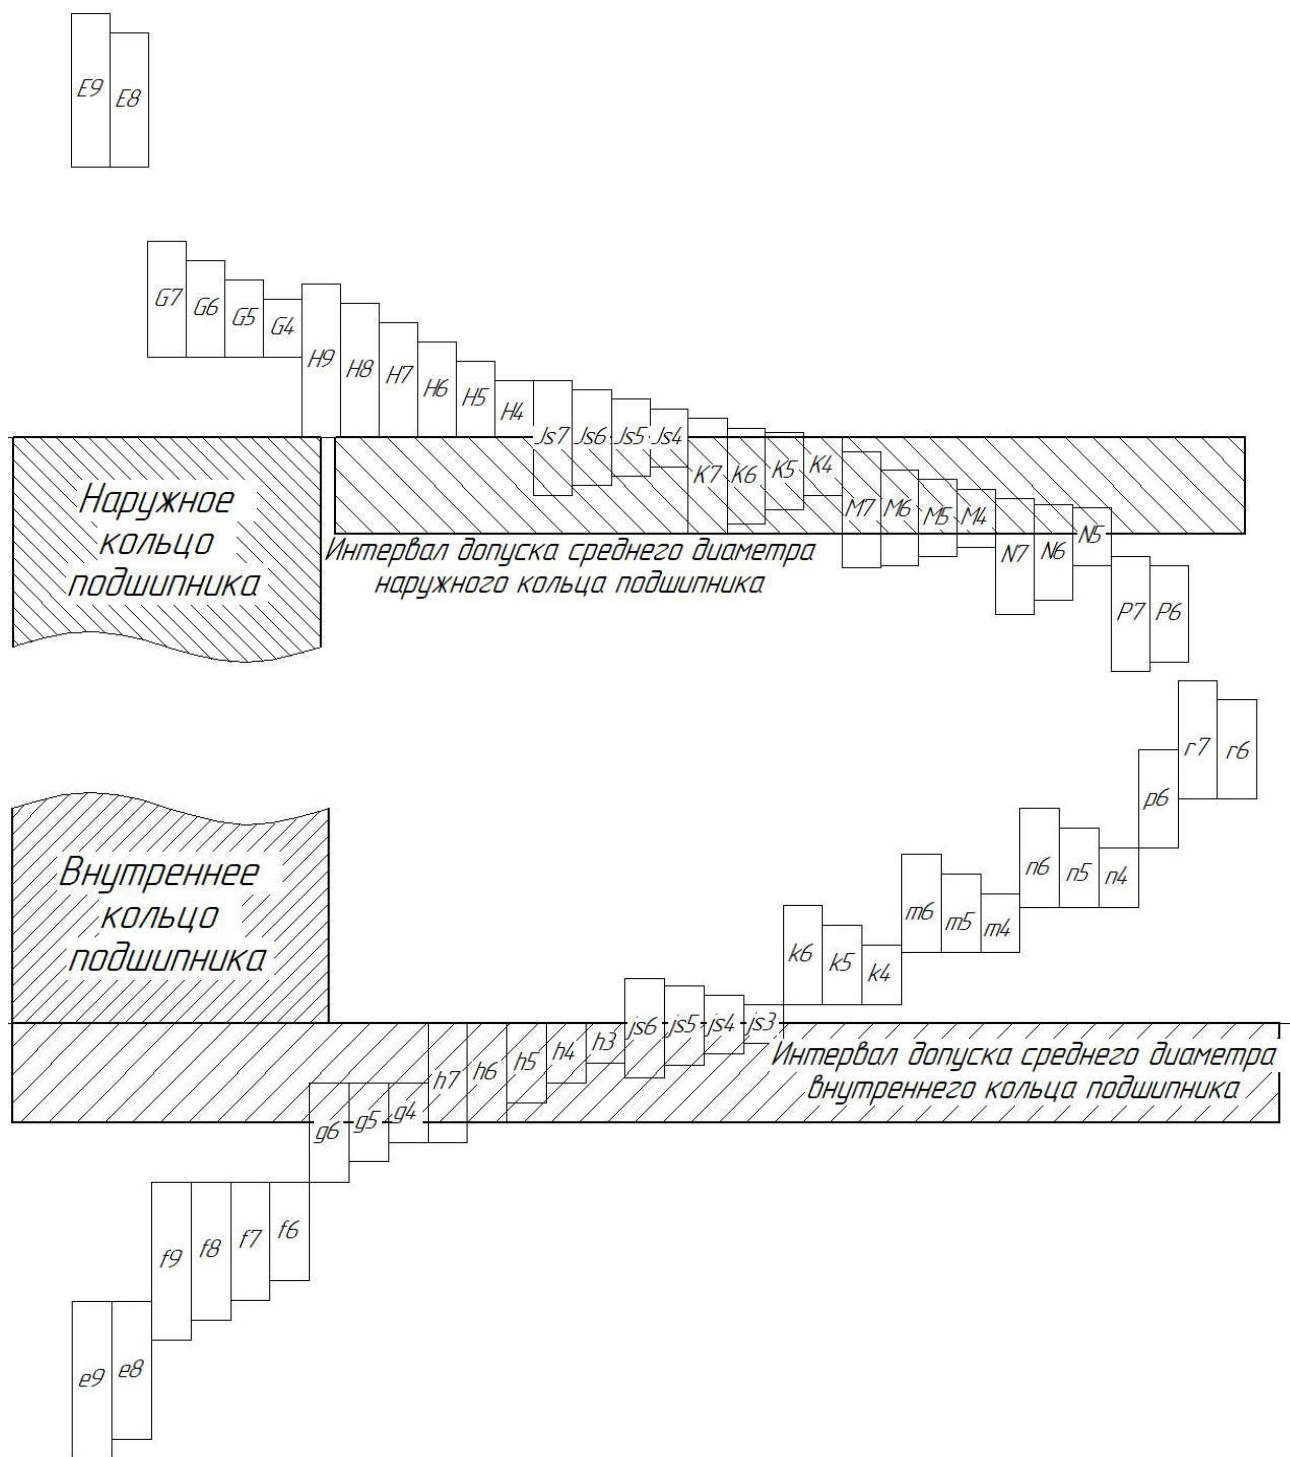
Рекомендуемые классы допусков для подшипников качения
